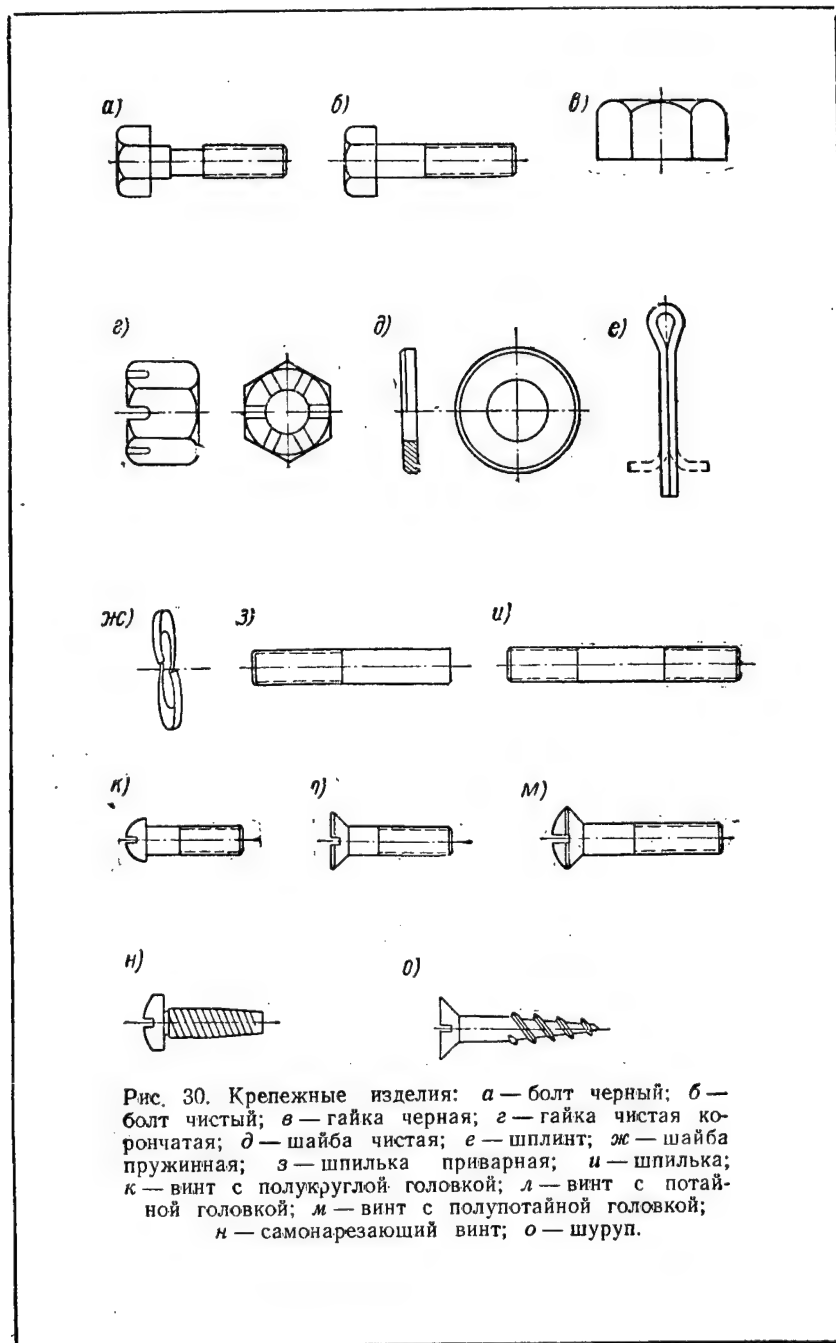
Крепежные изделия: а — болт черный; б — болт чистый; в — гайка черная; г — гайка чистая корончатая; д — шайба чистая; е — шплинт; ж — шайба пружинная; з — шпилька приварная; и — шпилька; к — винт с полукруглой головкой; л — винт с потайной головкой; м — винт с полупотайной головкой; н — самонарезающий винт; о — шуруп.
